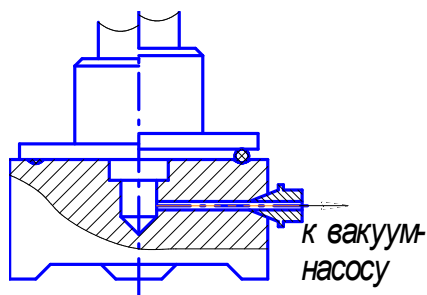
Схема специального приспособления – зажима с вакуумным креплением (правая часть – до закрепления, левая – после)
